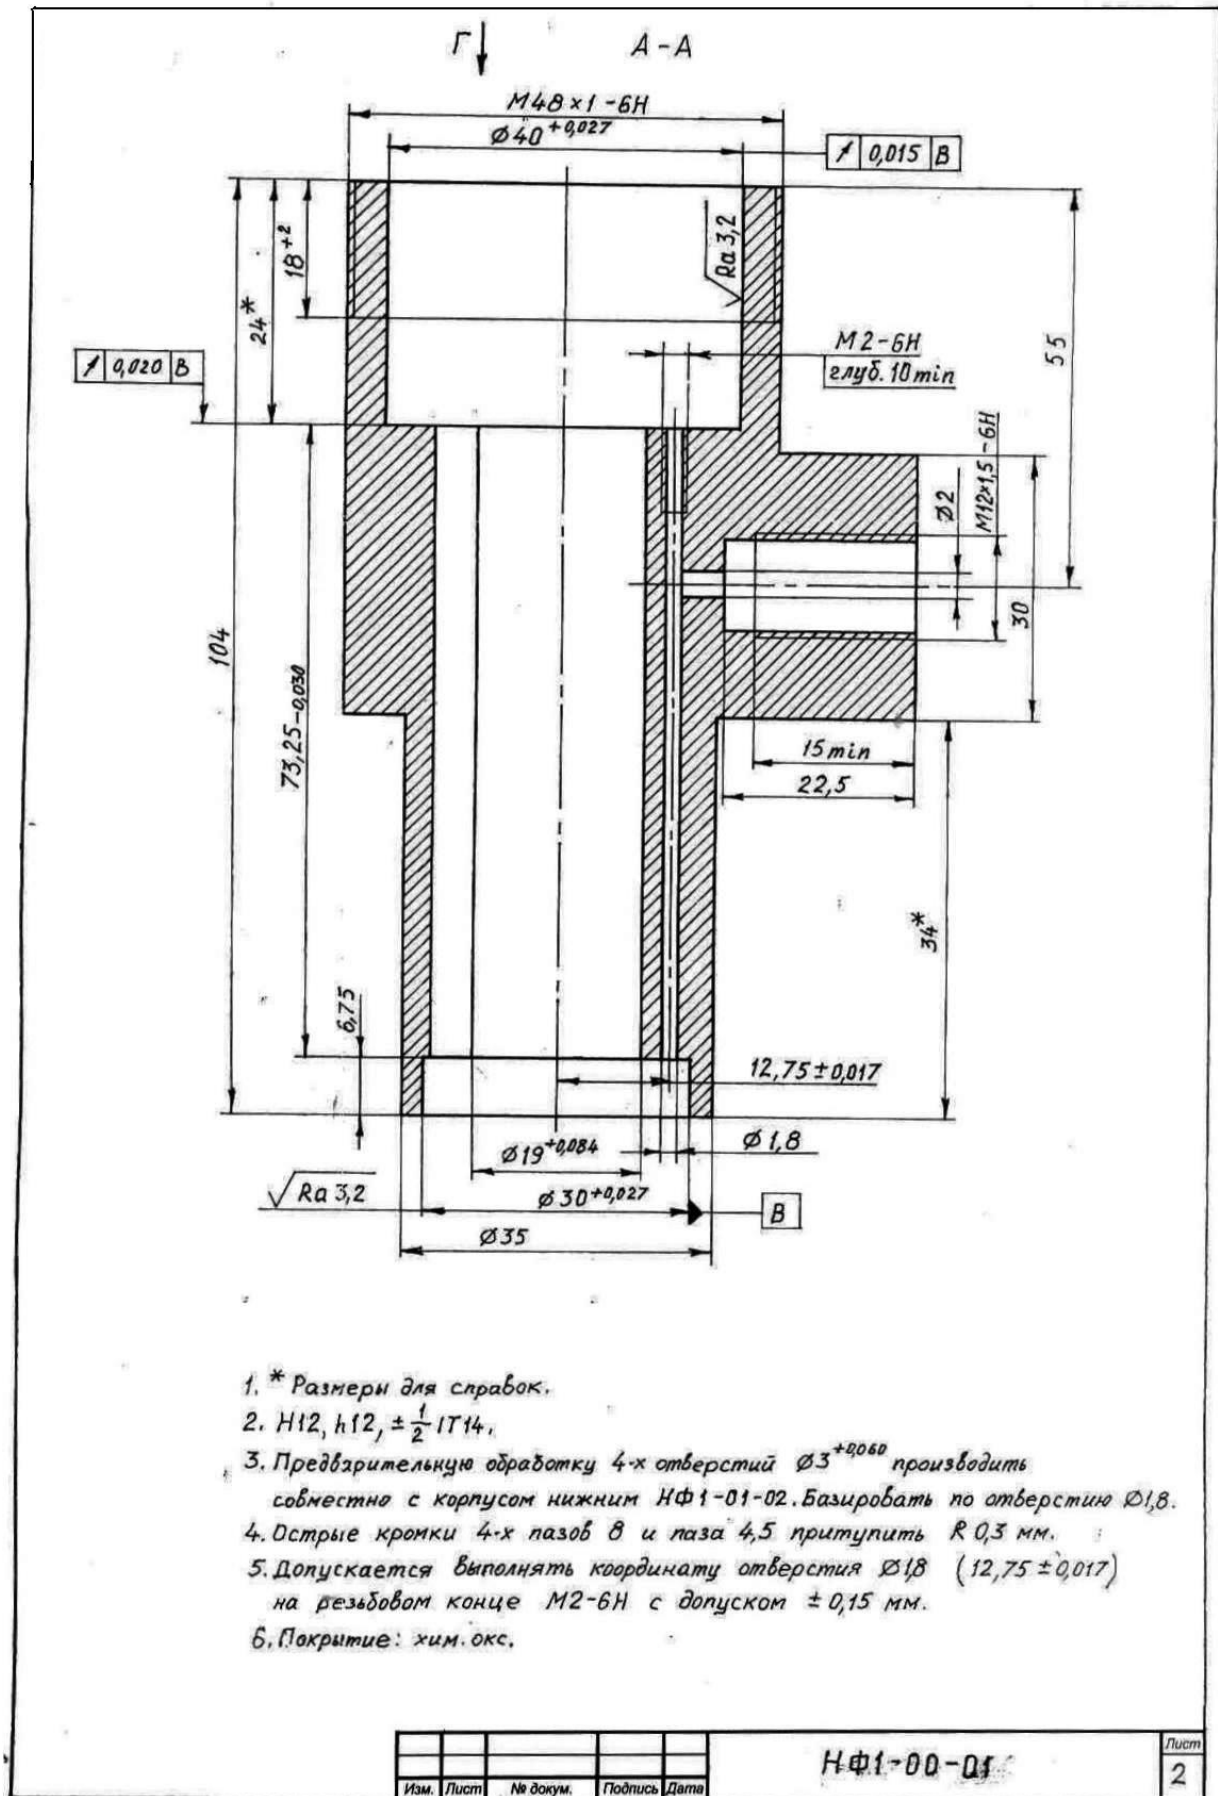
б. Пример выполнения рабочего чертежа детали «Корпус нижний»
